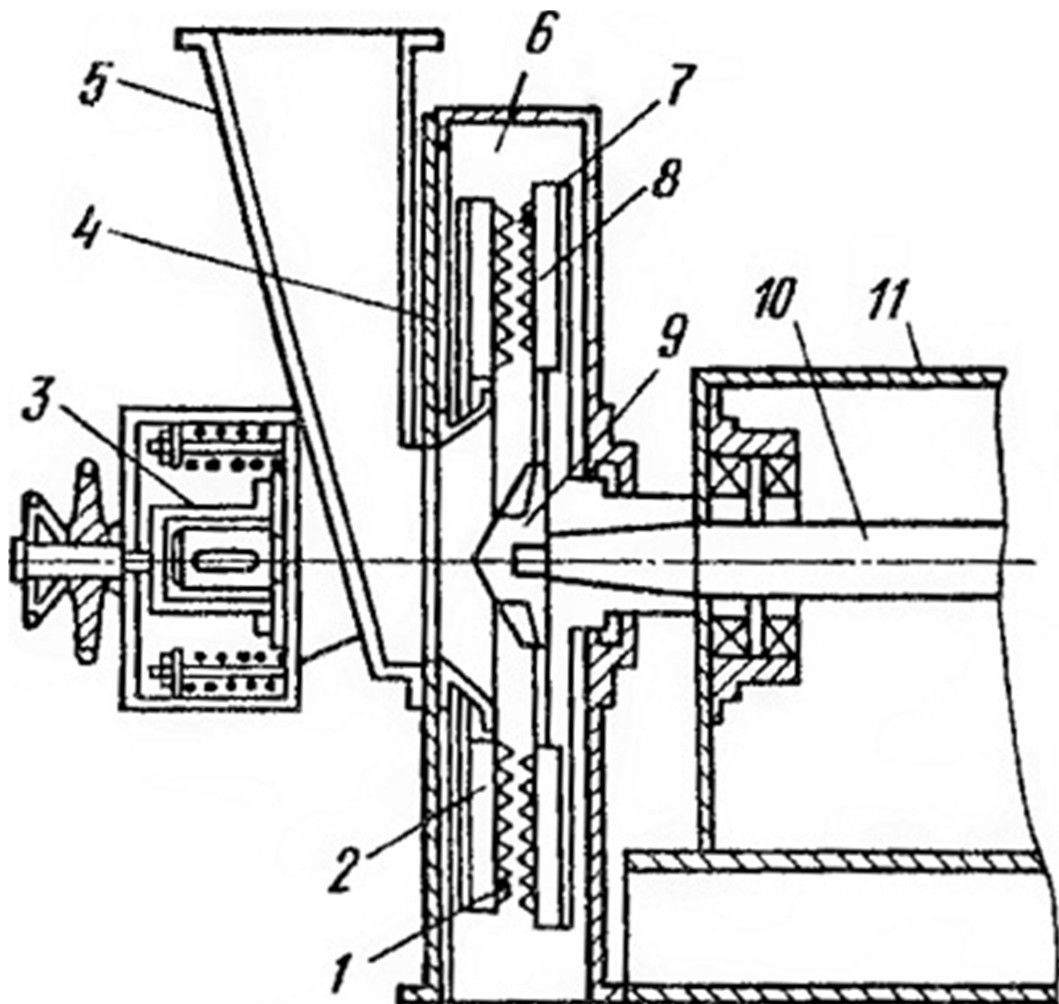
Дробарка марки ЗД2-Д-250
